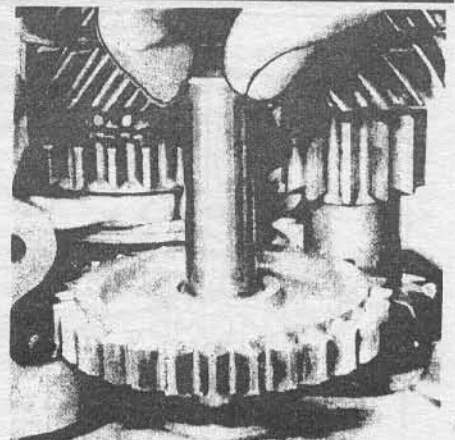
Установка вала и промежуточной шестерни заднего хода.
